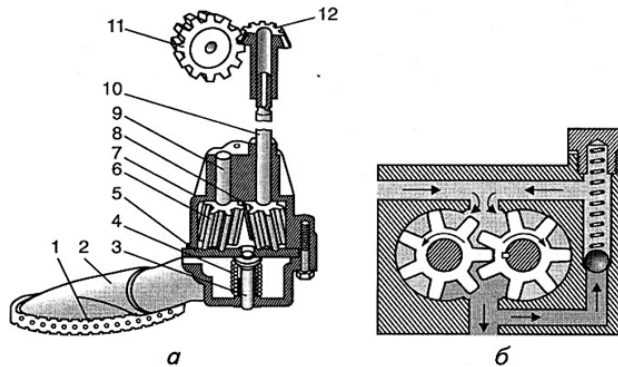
Шестеренчастий оливний насос двигуна автомобіля ВАЗ-2105:
